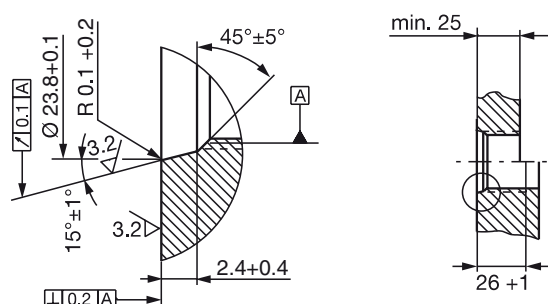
Einschraubloch M22×1.5 nach ISO 6149 O-Ring 19.3×2.2
